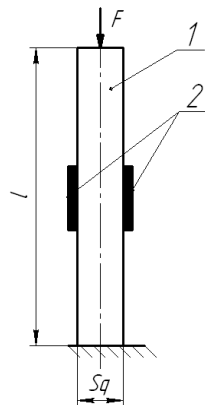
Стержневий механічний перетворювач сили з тензорезисторами
